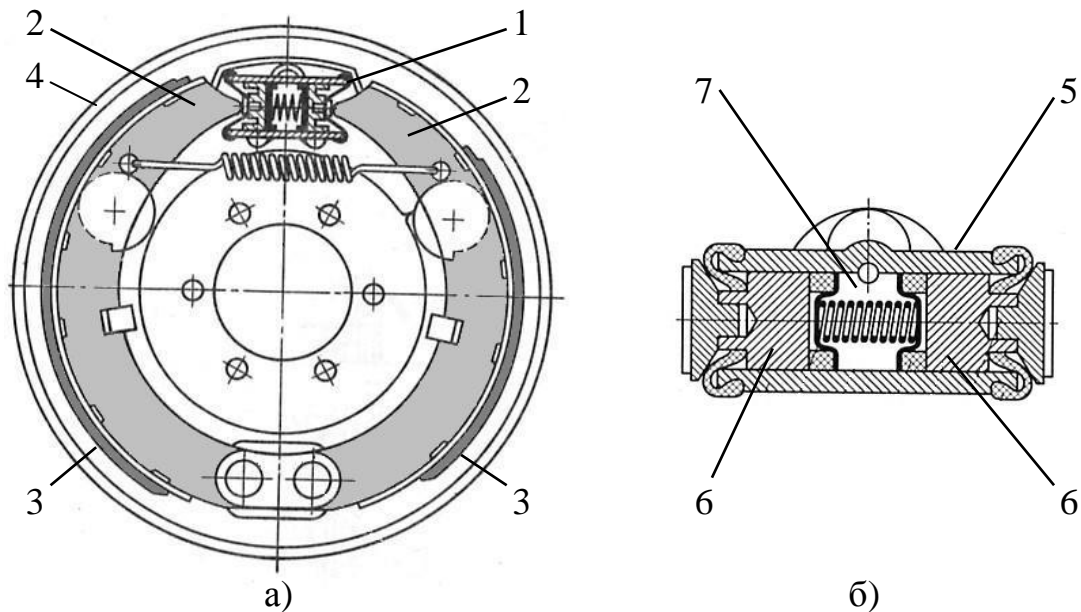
Барабанный тормозной механизм с поршневым разжимным устройством (а) и поршневое разжимное устройство (б): 1 – разжимное устройство; 2 – тормозные колодки; 3 – накладки тормозных колодок; 4 – тормозной барабан; 5 – цилиндр; 6 – поршни; 7 – полость
